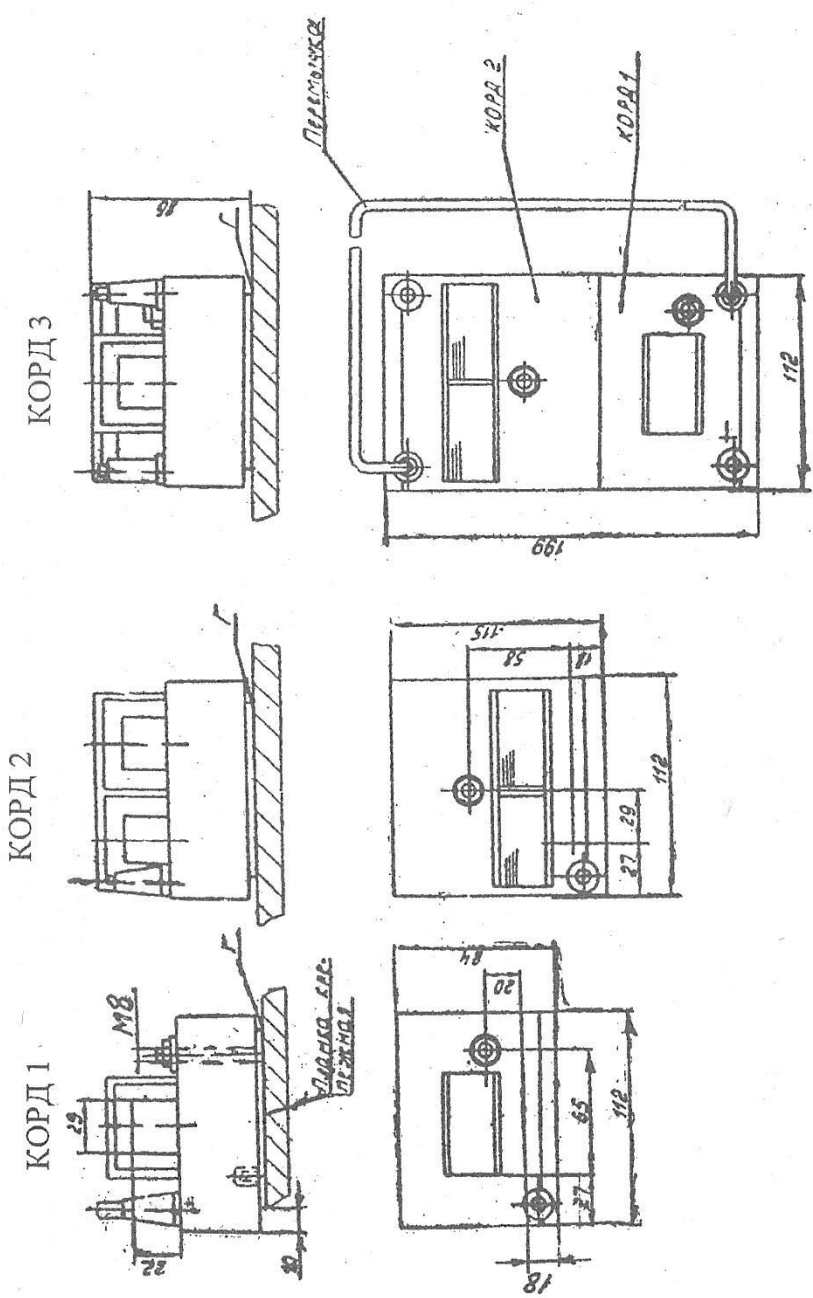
Габаритные размеры и установочные размеры аппаратов КОРД:
